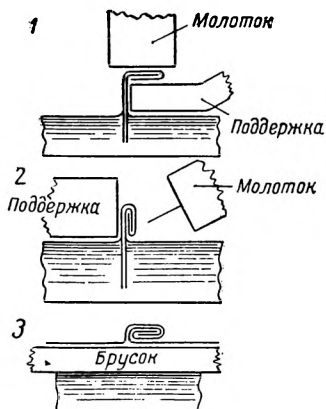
Заготовка двойного стоячего и двойного лежащего торцовых фальцев
